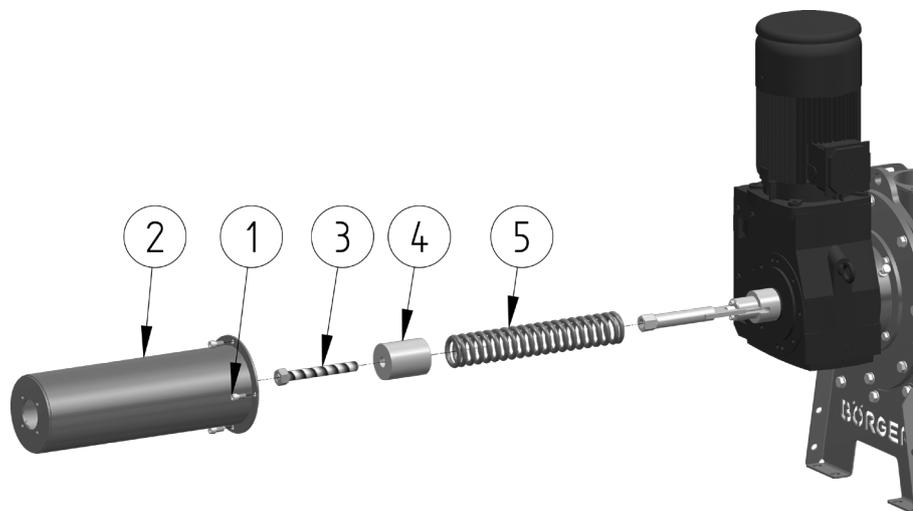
Unité de serrage à réglage mécanique
